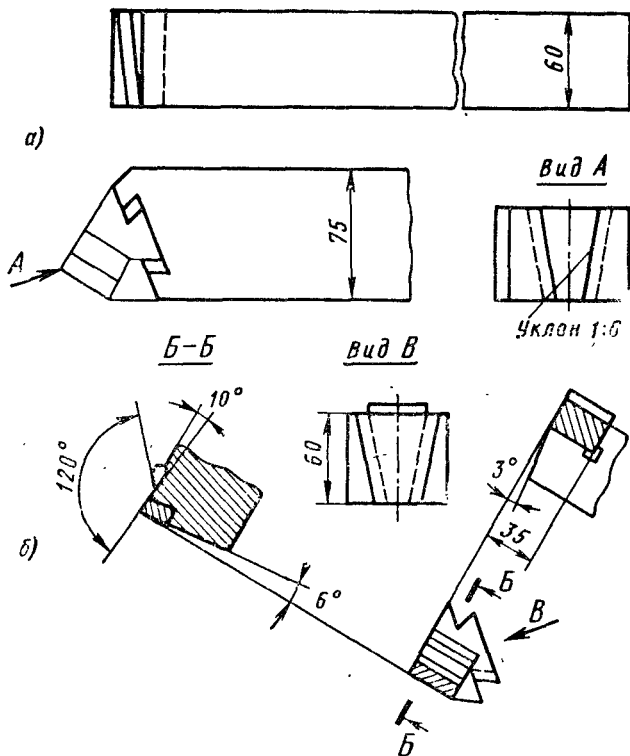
Сборный резец с клиновым креплением вкладыша конструкции Уралмашзавода:
